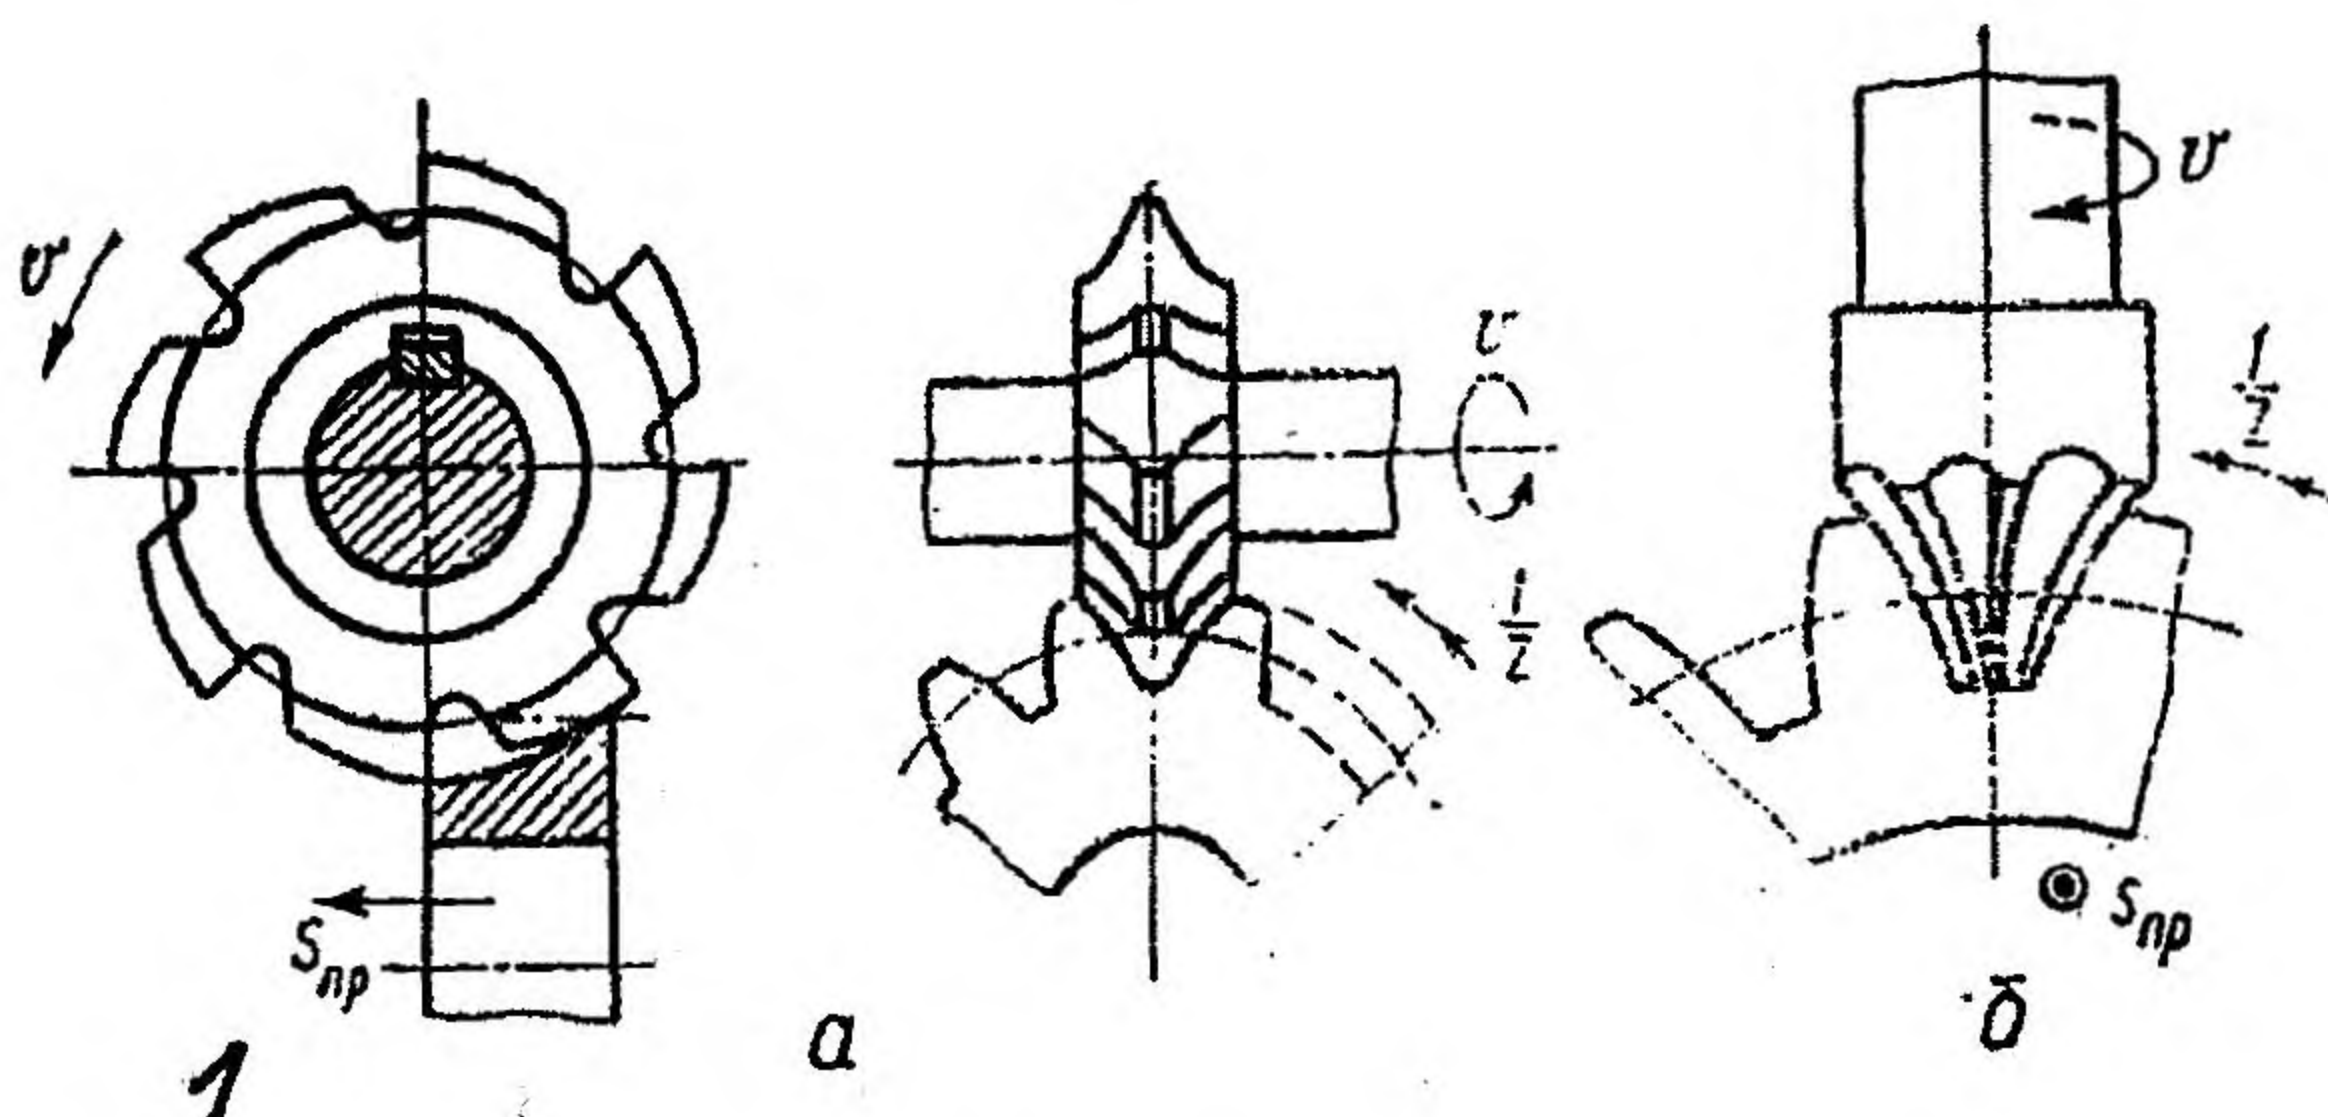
Схемы фрезерования зубьев методом копирования дисковой (а) и пальцевой (б) модульными фрезами
